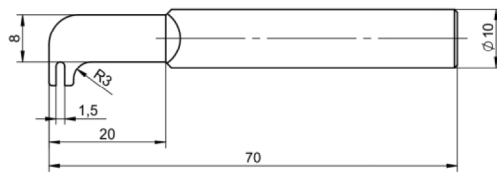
Massenelektrode Einstellwerkzeug Typ 1253A
